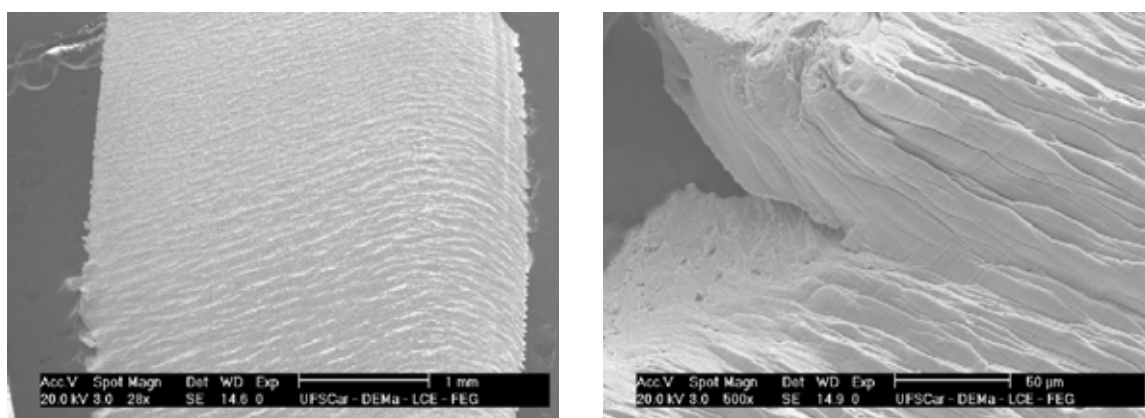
Cavaco extraído da amostra (A) sob a condição de usinagem C2.
